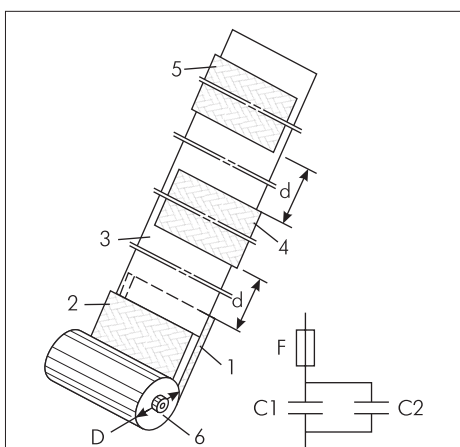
Схема защитной системы IPE силового металлопленочного конденсатора: 1, 2 — металлизированная лента обкладок; 3 — отрезок пленки; 4, 5 — лист фольги; 6 — рулон обмотки секции; C1 — основной, самовосстанавливающийся конденсатор; C2 — дополнительный, не самовосстанавливающийся конденсатор; F — внешний быстродействующий плавкий предохранитель
